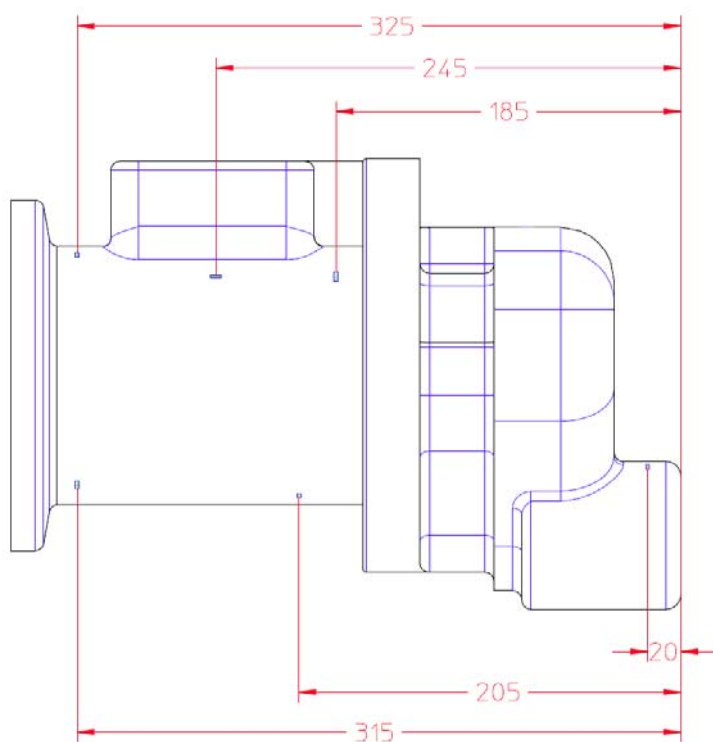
Bemaßung der Messstellen Seitenansicht Hauptläufer
